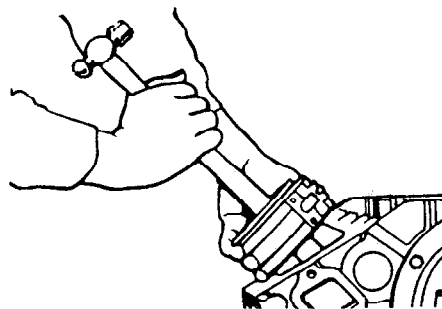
Instalación del pistón en el cilindro con un compresor de anillos
